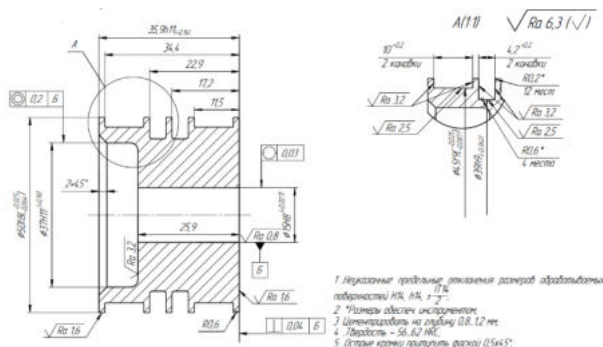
Чертеж поршня силового гидроцилиндра с конструктивными изменениями
